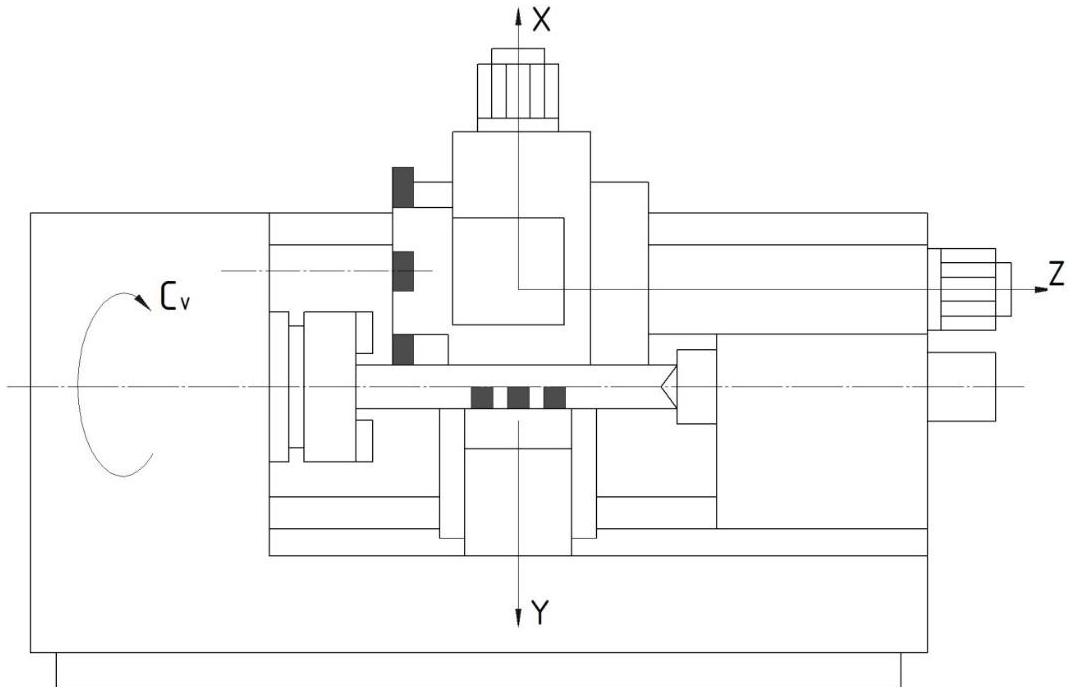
Компонівка токарного верстата (Варіант 4)
